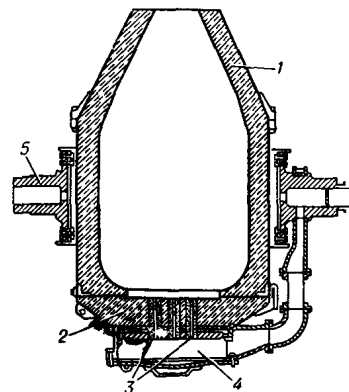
Схема бессмеровского конвертера: 1 — корпус; 2 — днище; 3 — фурмы; 4 — воздушная коробка; 5 — цапфы для поворота конвертера при заливке и выпуске металла.
